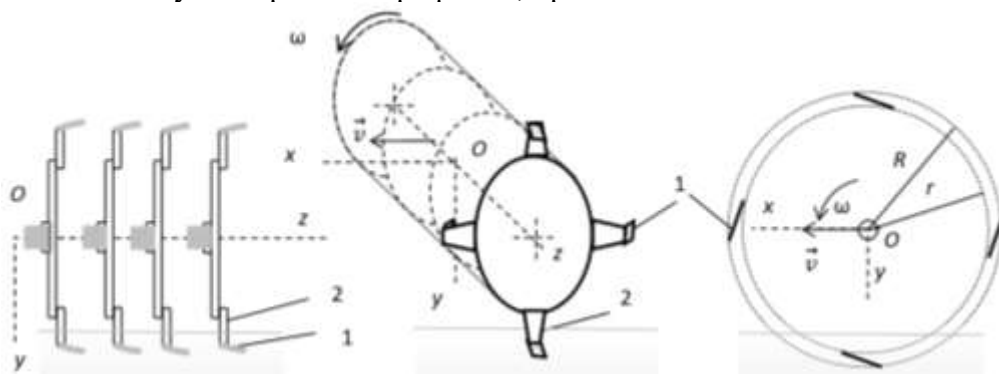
Барабан фрезы с ножами 1 и боковинами с режущими кромками 2
